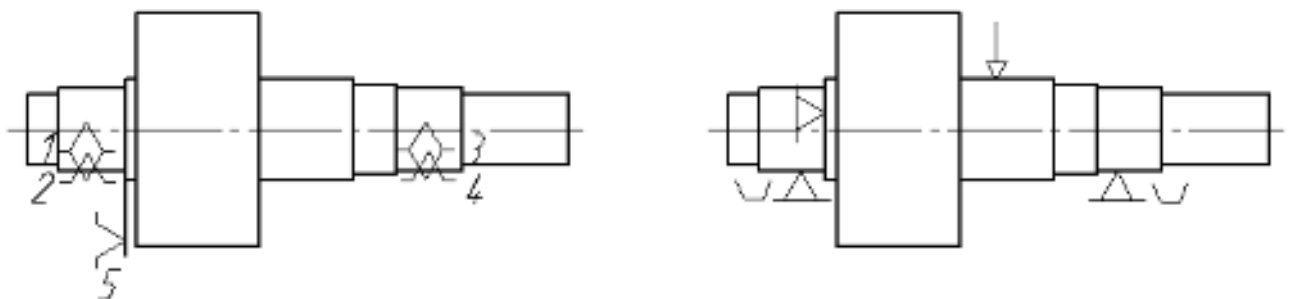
Схема базування і закріплення деталі на шпонково-фрезерній операції
